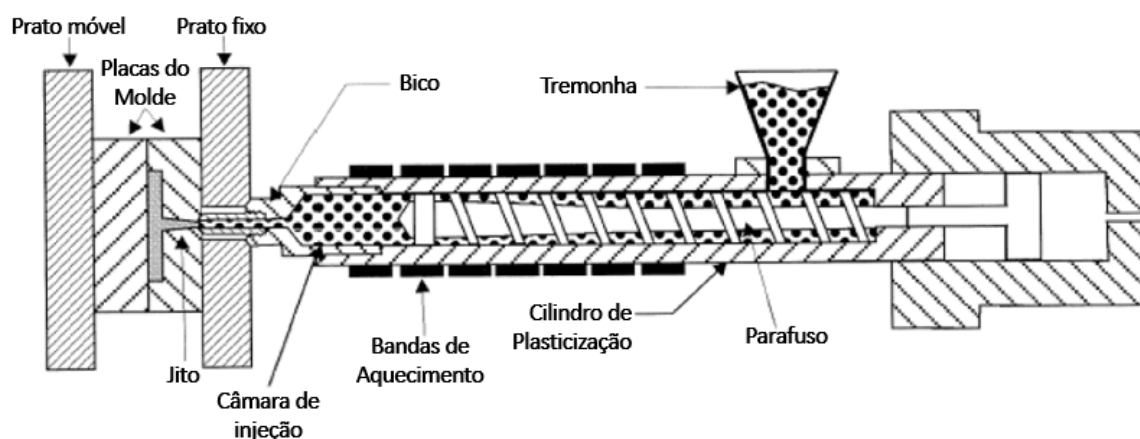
Cilindro de Injeção e pormenor de molde - adaptada de [8]
